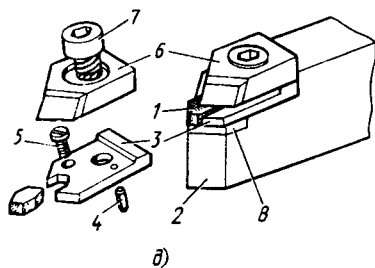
Конструкции резцов с режущими элементами из алмаза и композита:
